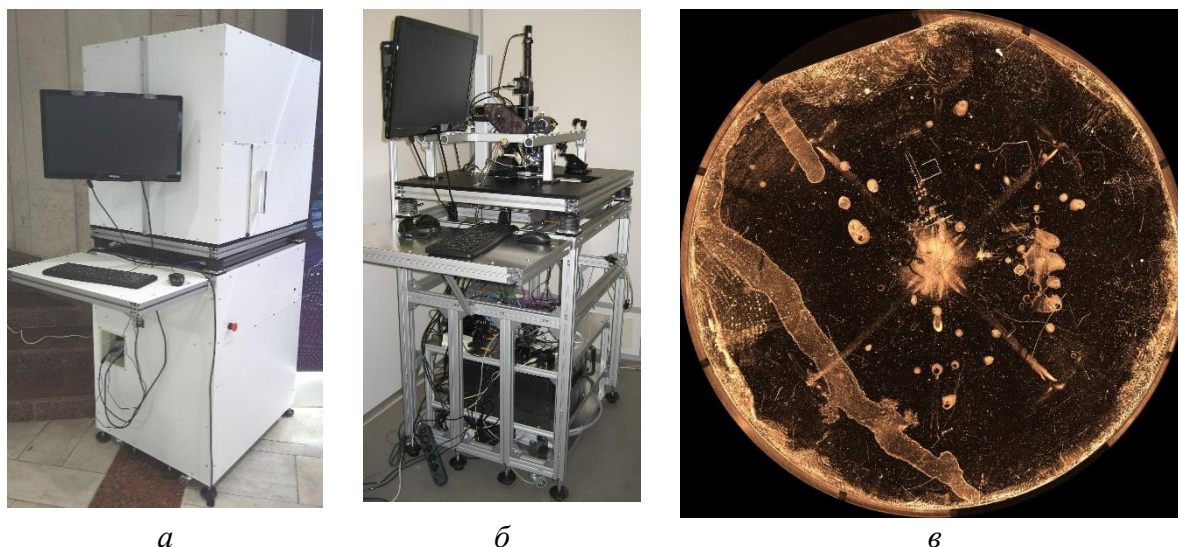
Установка ОАТДППП: *а* – общий вид установки; *б* – установка без защитного кожуха; *в* – карта дефектов тестового образца.
